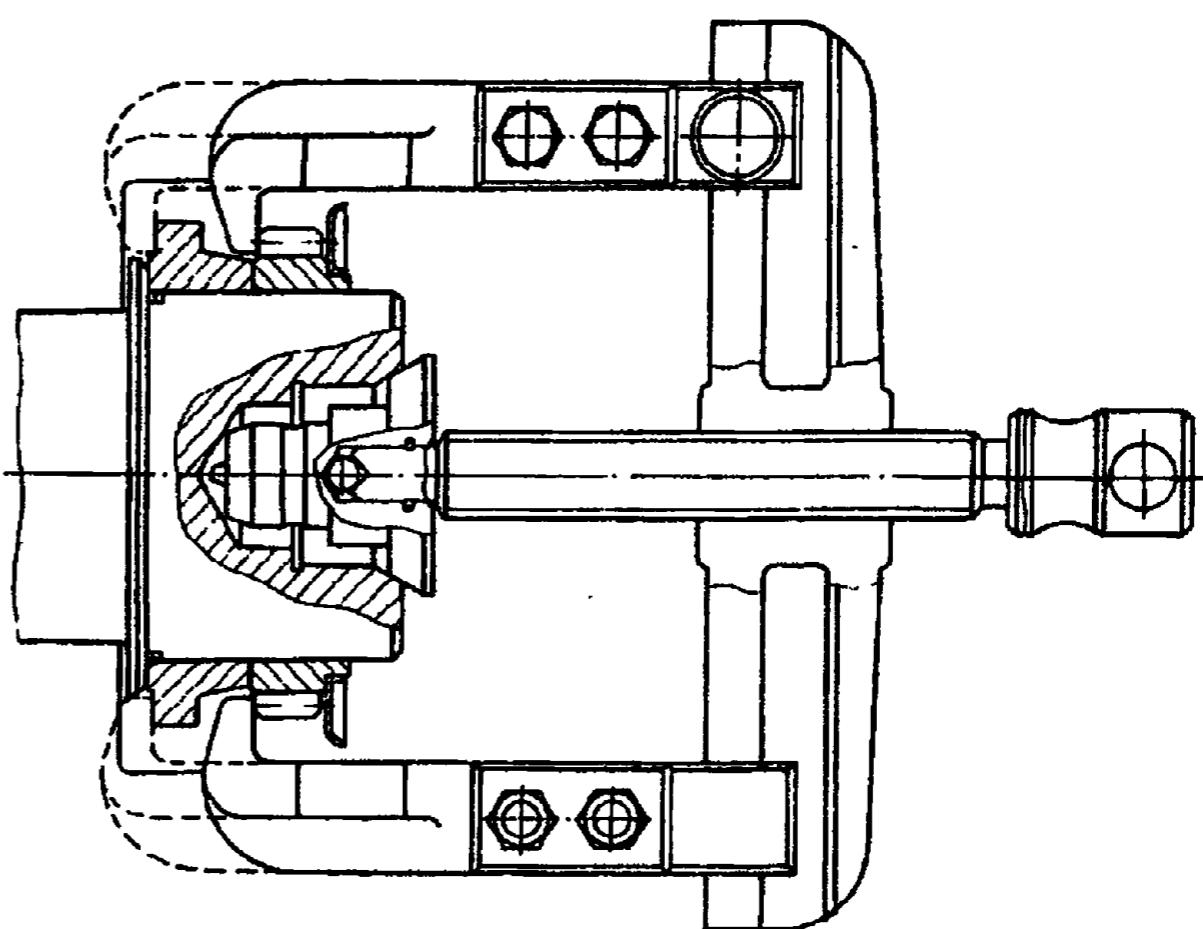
Съемник шестерен и противовесов коленчатого вала из комплекта Н801-02
